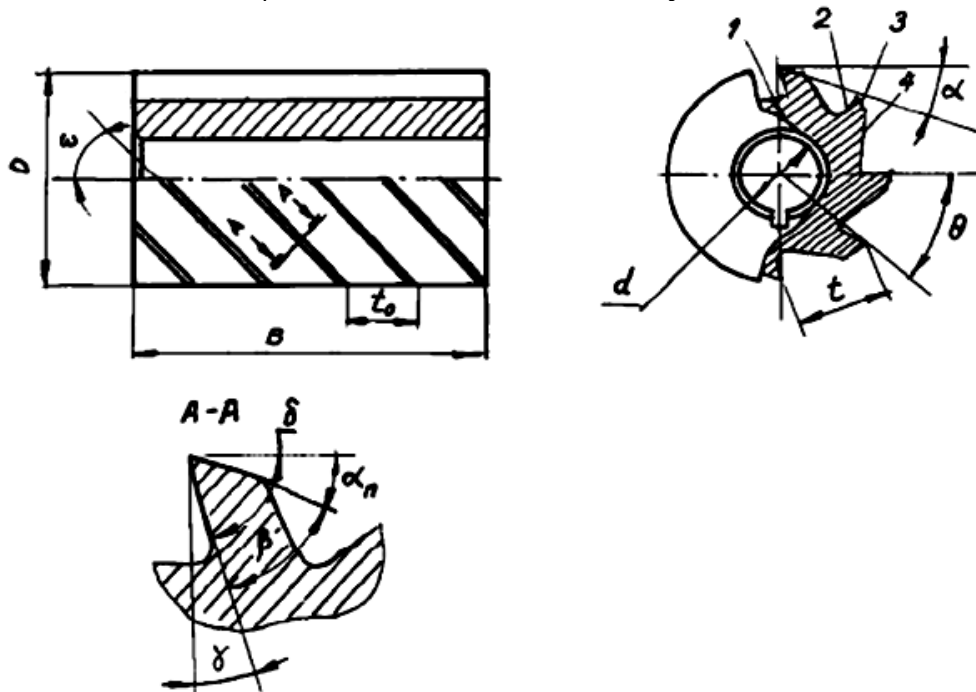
Конструкция и геометрия цилиндрической фрезы
